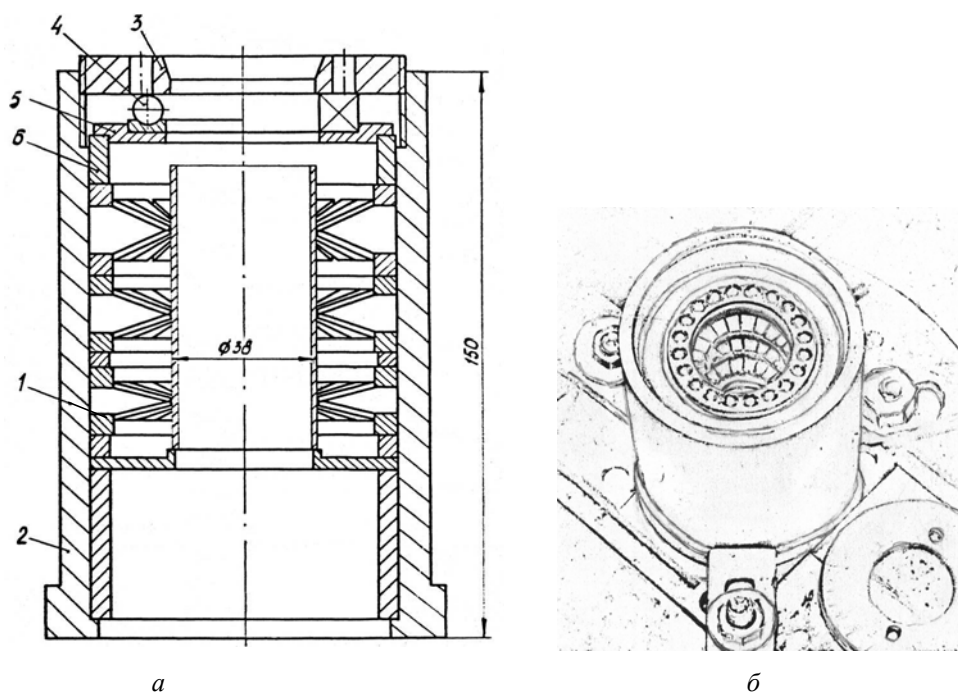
Зажимное приспособление для хонингования: а – конструкция; б – общий вид
